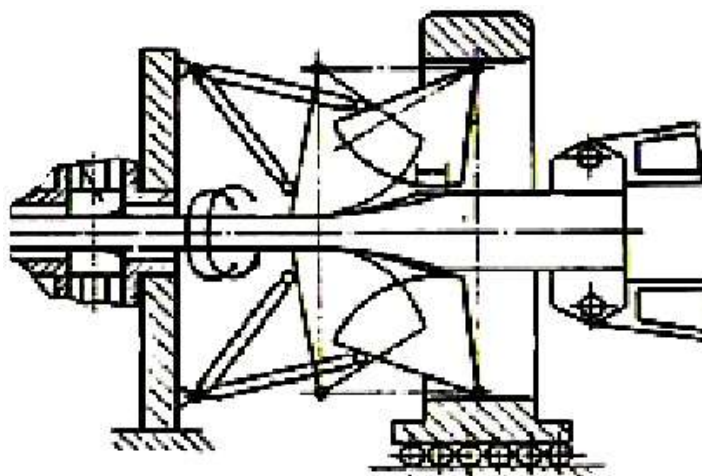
Машина прокатки-ковки конструкции ЧПИ
